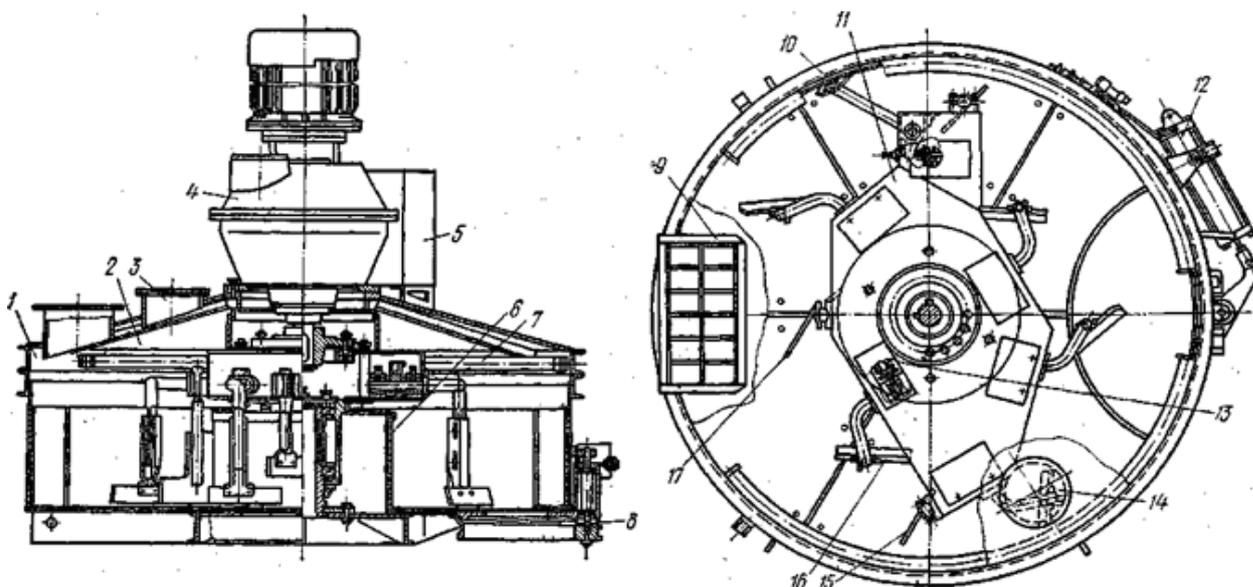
Бетоносмеситель СБ-138Б: 1 — корпус-чаша, 2 — крышка, 3 — вытяжной патрубков, 4 — мотор-редуктор, 5 — пульт управления, 6 — центральный стакан, 7 — сливная труба, 8 — разгрузочный затвор, 9 — загрузочный люк для заполнителей, 10 — наружный очистной скребок, 11 — ротор, 12 — пневмоцилиндр, 13 — пружина, 14 — загрузочный патрубков для цемента, 15 — верхняя лопасть, 16 — донная лопасть, 17 — внутренний очистной скребок.
